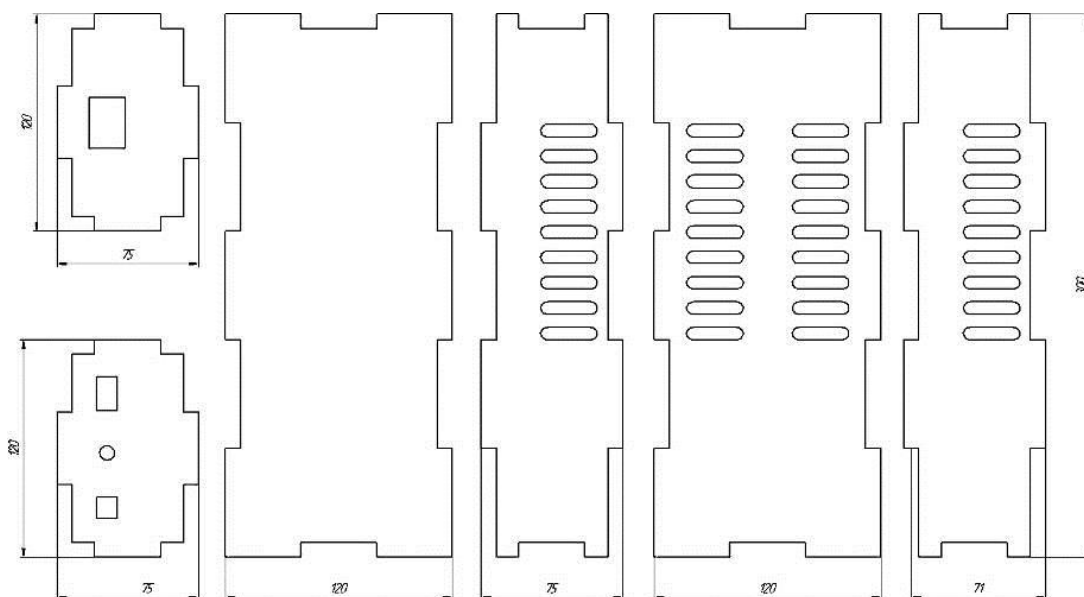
Креслення корпусу блоку живлення портативної рентгентелевізійної установки
